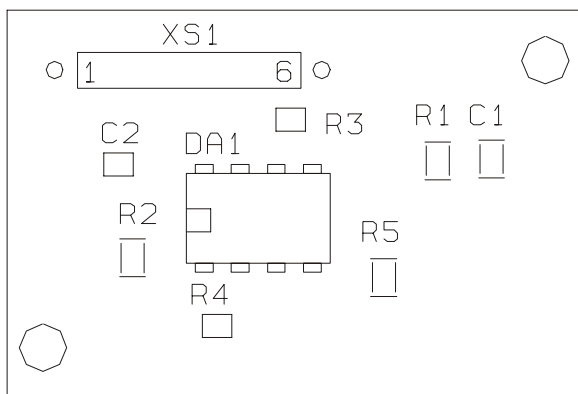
Сборочный чертеж платы датчика ФСТ (СО). Сторона пайки
